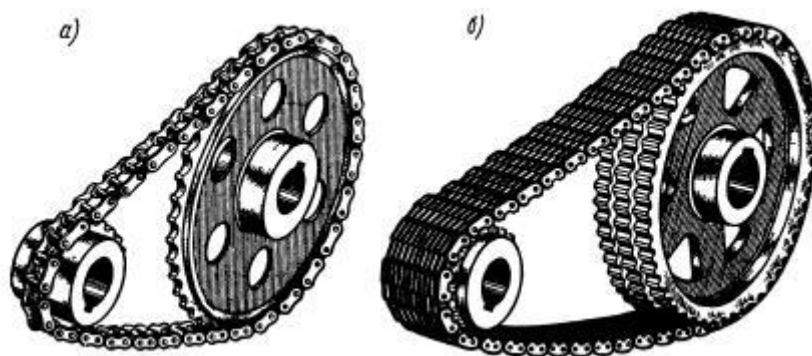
Цепная передача: а – роликовой цепью, б – зубчатой цепью.
